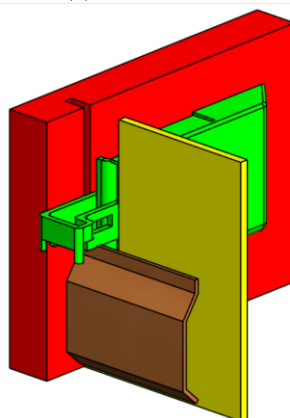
Взаимное расположение навеса и планки для навеса относительно конструкции корпуса.
